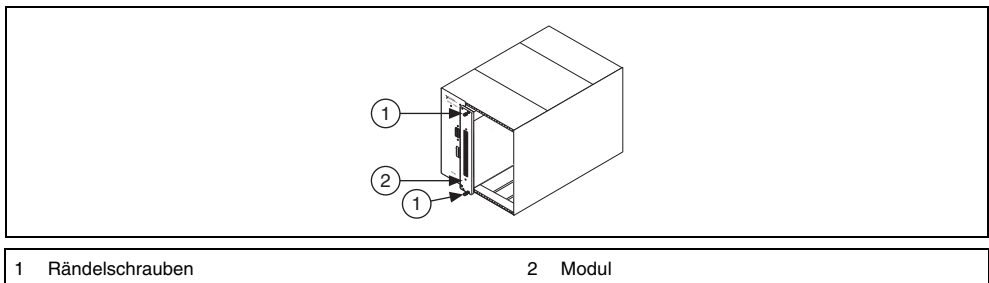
Einstecken eines SCXI-Moduls in ein Chassis
